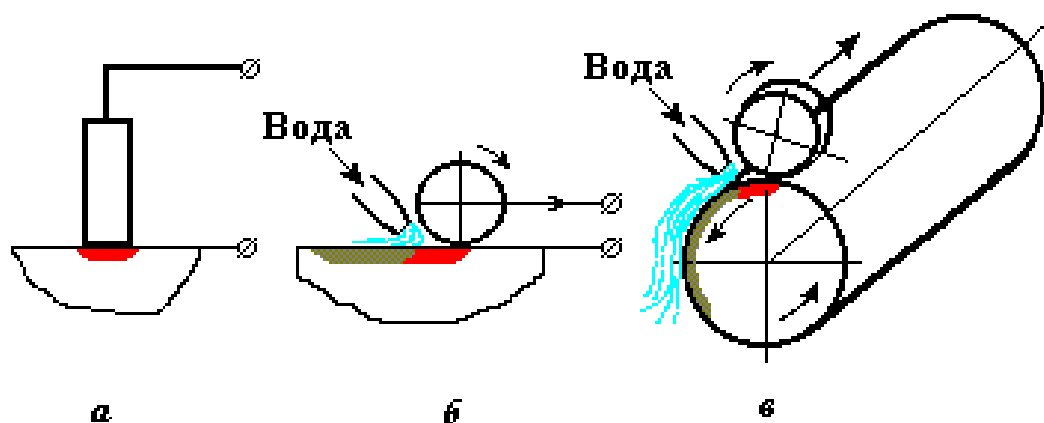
Схемы контактной закалки стали: *а* - с точечным контактом; *б*- роликовый способ нагрева и закалки поверхностей; *в* - нагрев и закалка цилиндрических поверхностей
